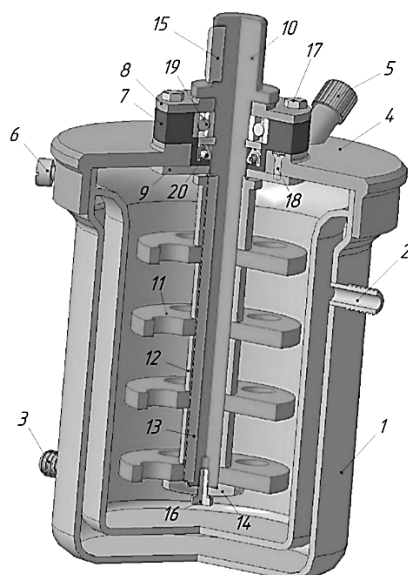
Робоча камера бісерного млина з дисковими робочими органами: 1 — стакан; 2, 3 — патрубки для охолоджувальної рідини; 4 — кришка; 5 — пробовідбірник; 6 — фіксатор кришки; 7 — підшипниковий вузол; 8 — кришка; 9 — шайба; 10 — вал; 11 — диск; 12 — втулка; 13 — шпонка; 14 — шайба; 15 — шпонка; 16—18 — гвинти; 19 — підшипник
